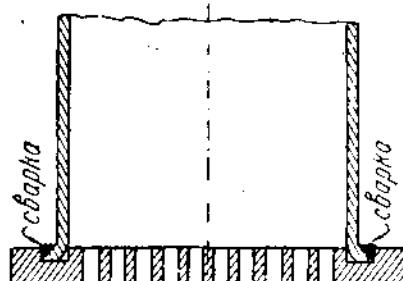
Способ сварки, применяемый в охладителях для рассола.
